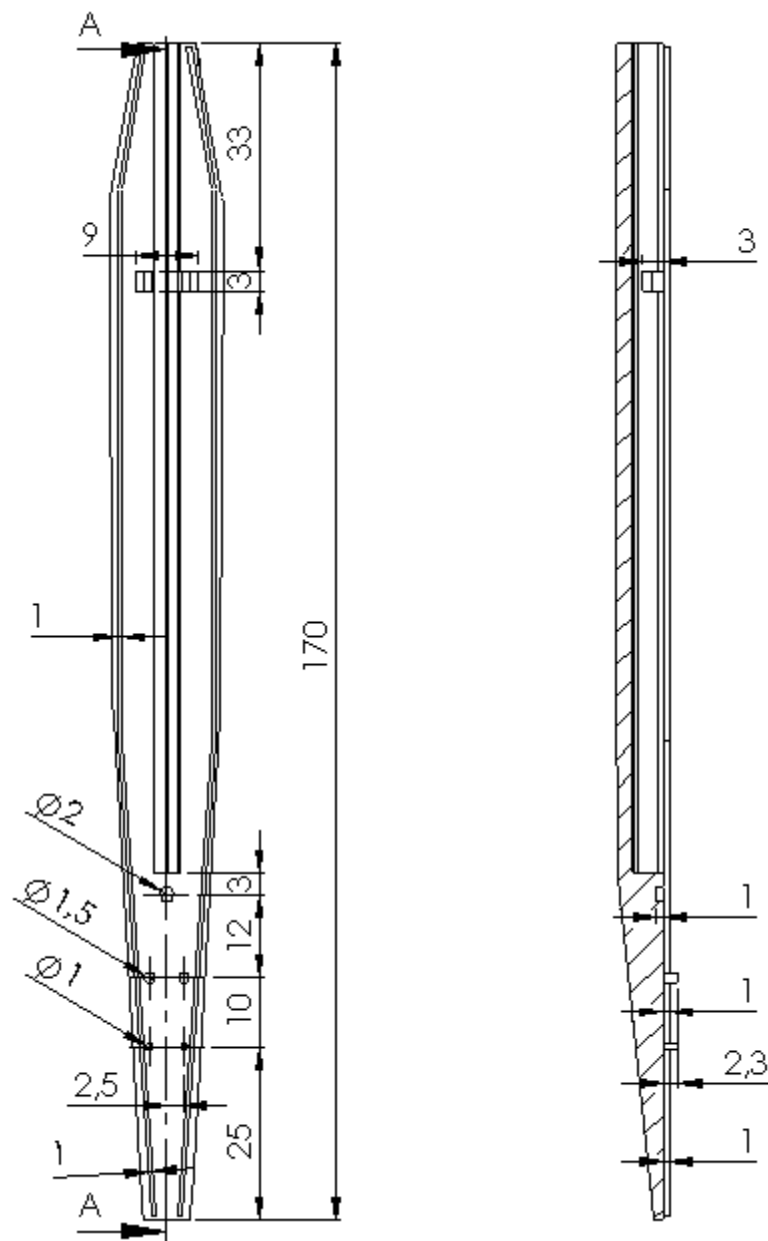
Carcassa inferior. Vista de de planta (figura de la dreta) i secció A-A de la vista de planta (figura de l'esquerra).
